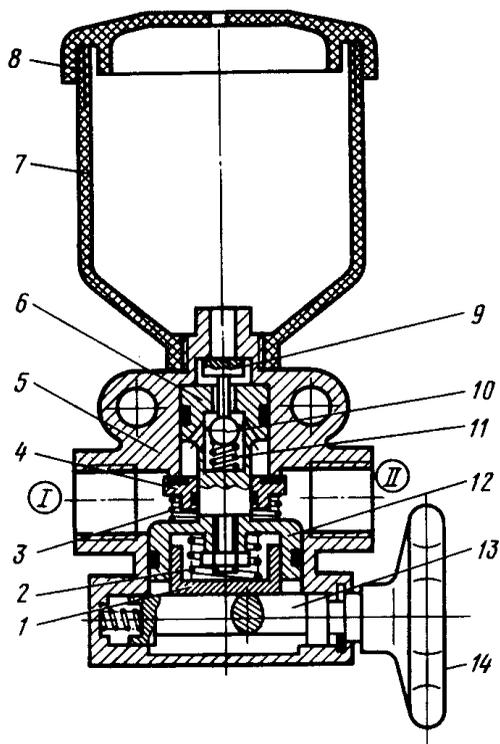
Насосный предохранитель против замерзания с автоматическим управлением: 1 – вход от компрессора; II – выход в ресиверы привода; 1 – тарелка пружины; 2 – пружина поршня; 3 – пружина выпускного клапана; 4 – выпускной клапан; 5 – корпус; 6 – верхняя головка поршня; 7 – бачок для спирта; 8 – крышка; 9 – шток; 10 – впускной клапан; 11 – пружина впускного клапана; 12 – нижняя головка поршня; 13 – кулачок; 14 – рукоятка
